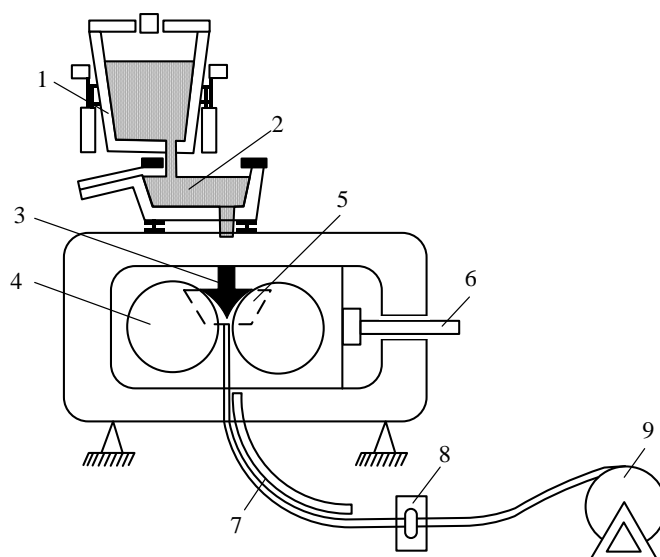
Схема двухвалковой МНЛЗ: 1 – ковш; 2 – разливочный узел; 3 – погружной стакан; 4 – валки; 5 – уплотнение; 6 – регулятор нагрузки; 7 – направляющий желоб; 8 – приемные валки; 9 – статыватель
